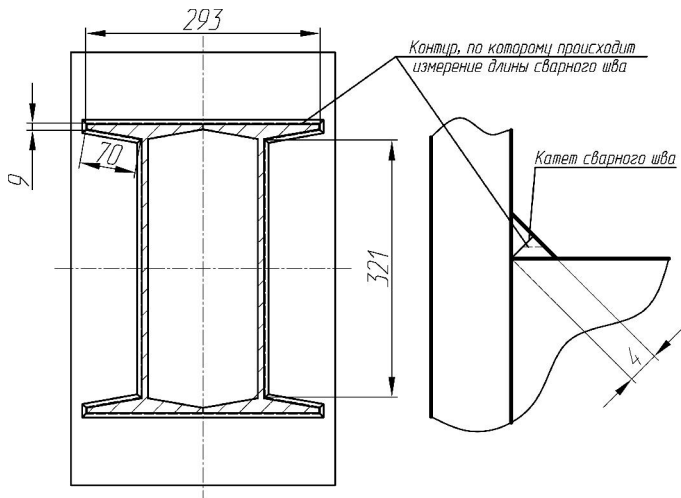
Расположение сварного шва и величина его катета
